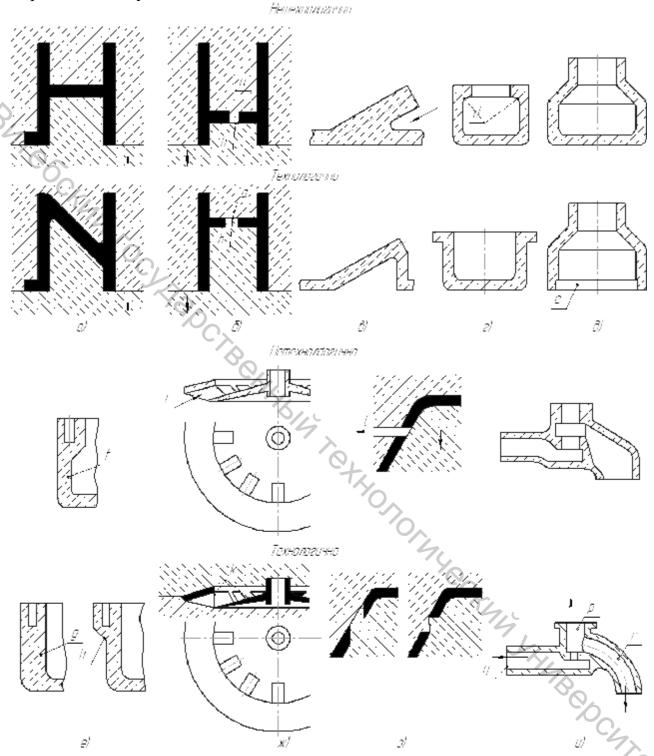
Примеры выбора технологичного варианта конструкции отливки
